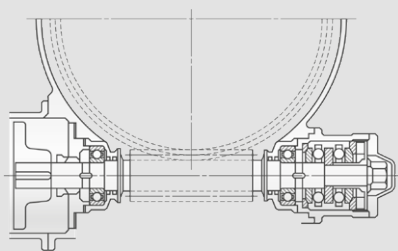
Установка преднатяга упорных шарикоподшипников (с помощью пружины)
